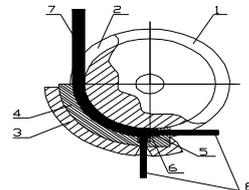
Принципиальная схема реализации процесса непрерывного прессования по спо- собу Конформ: 1 – рабочее колесо; 2 – коль- цевая канавка; 3 – башмак; 4 – кольцевая вставка; 5 – вставка; 6 – матрица; 7 – за- готовка; 8 – изделие
